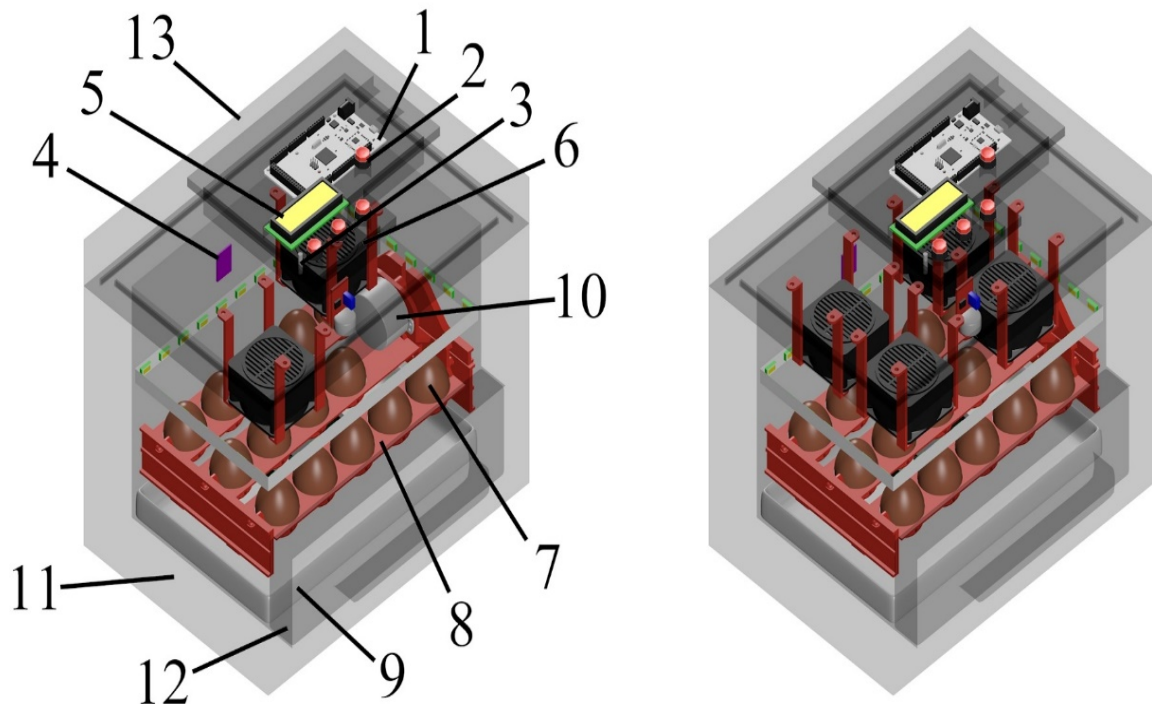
Лабораторный образец инкубатора с двумя и четырьмя нагревателями:
